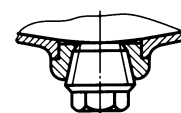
Штамповсварной защитный кожух
